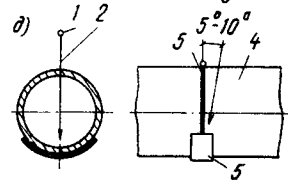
Схема испытания швов сварных угловых соединений (обозначения те же, что и на рис. 11.13)
